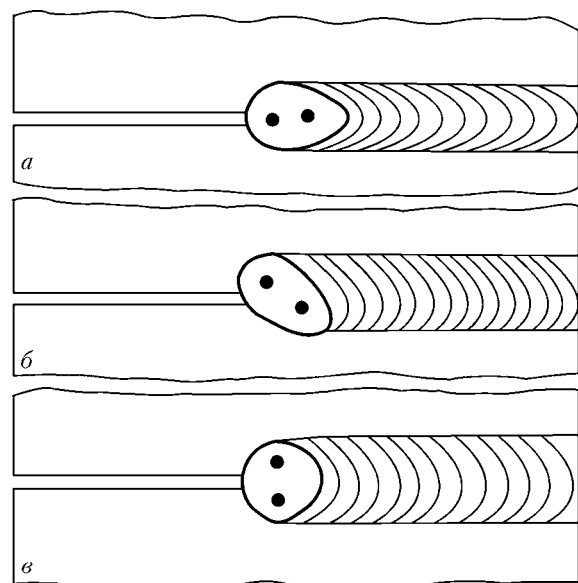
Схема расположения электродных проволок при двухдуговой сварке: а — продольное; б — под углом 45°; в — поперечное
